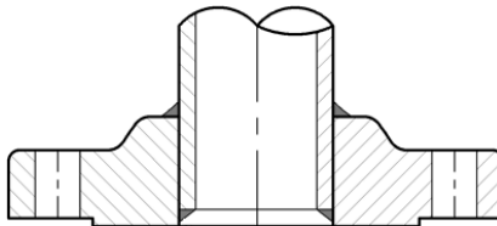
Накладной фланец с двойной сваркой
